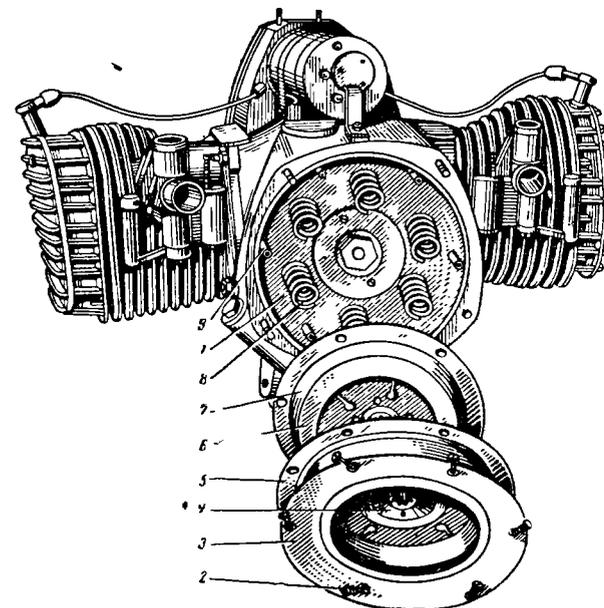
Установка сцепления: 1—маховик; 2—винт; 3—диск ведущий упорный; 4—диск ведомый в сборе с маслоотражателем; 5—диск ведущий промежуточный; 6—диск ведомый в сборе; 7—диск ведущий нажимной; 8—пружина; 9—палец маховика.
